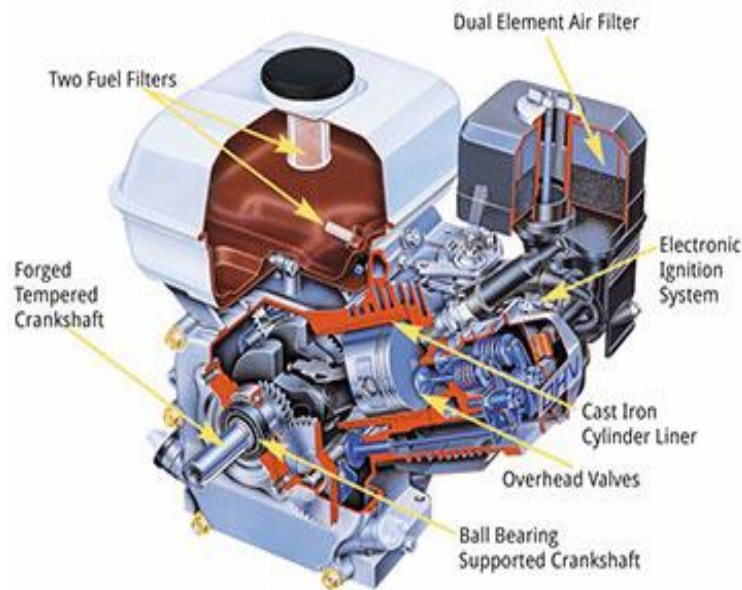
VISTA EXPLODIDA DO MOTOR GX390 - (FONTE: MANUAL HONDA)
